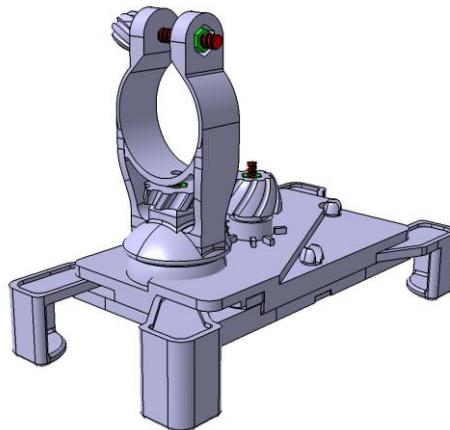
Colocando el conjunto de giro en el resto del ensamblaje.
